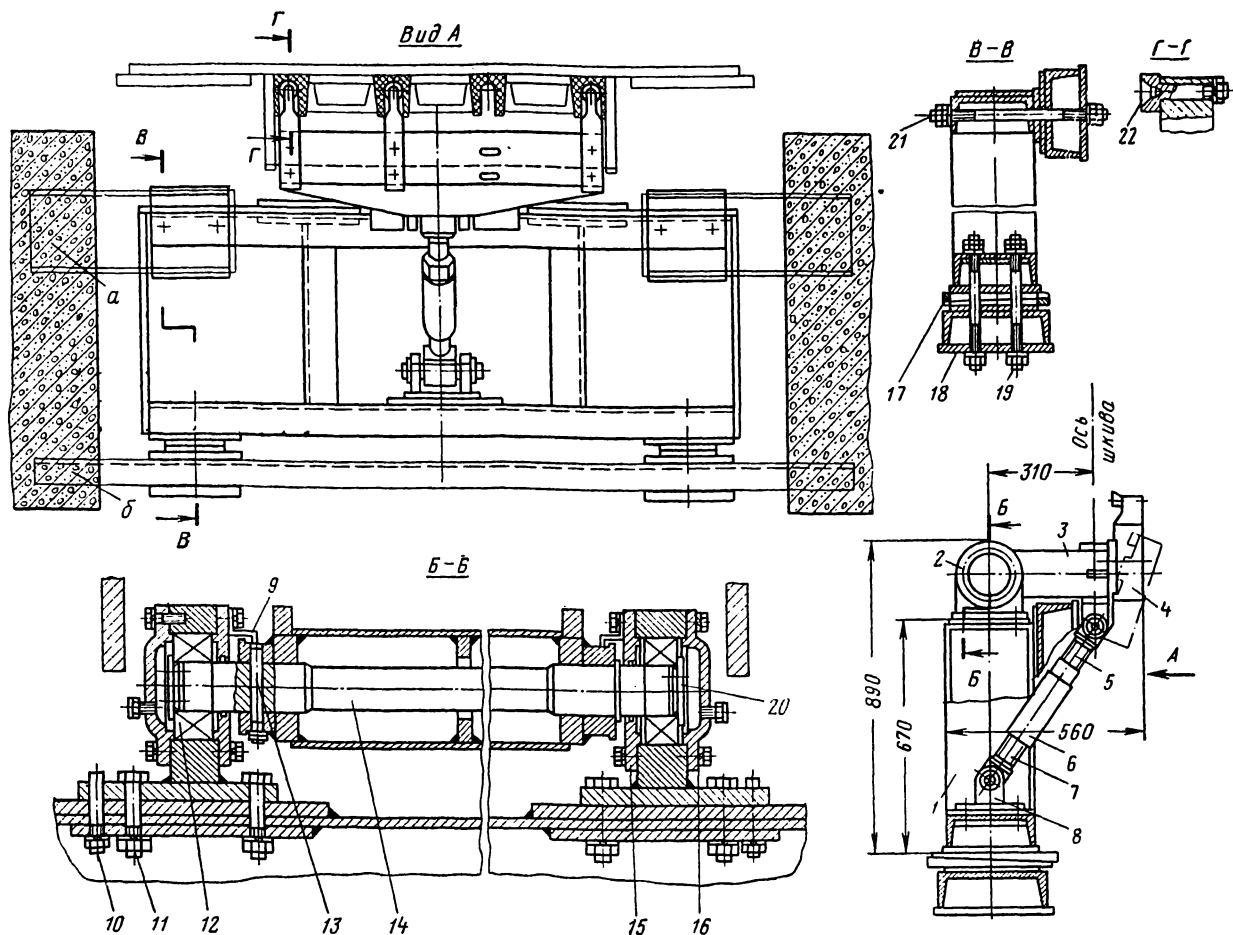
Приспособление для нарезки канавок на футеровке
